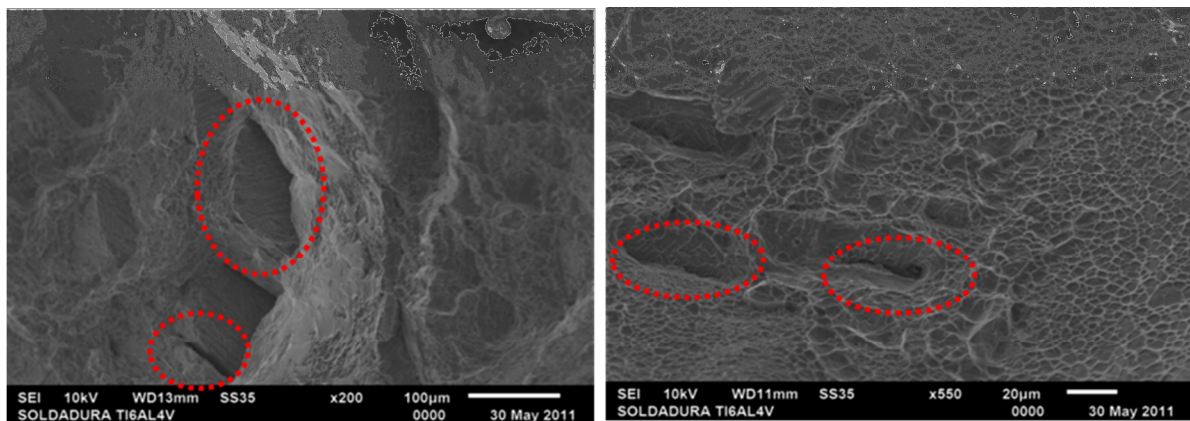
Falta de fusión de la soldadura.
